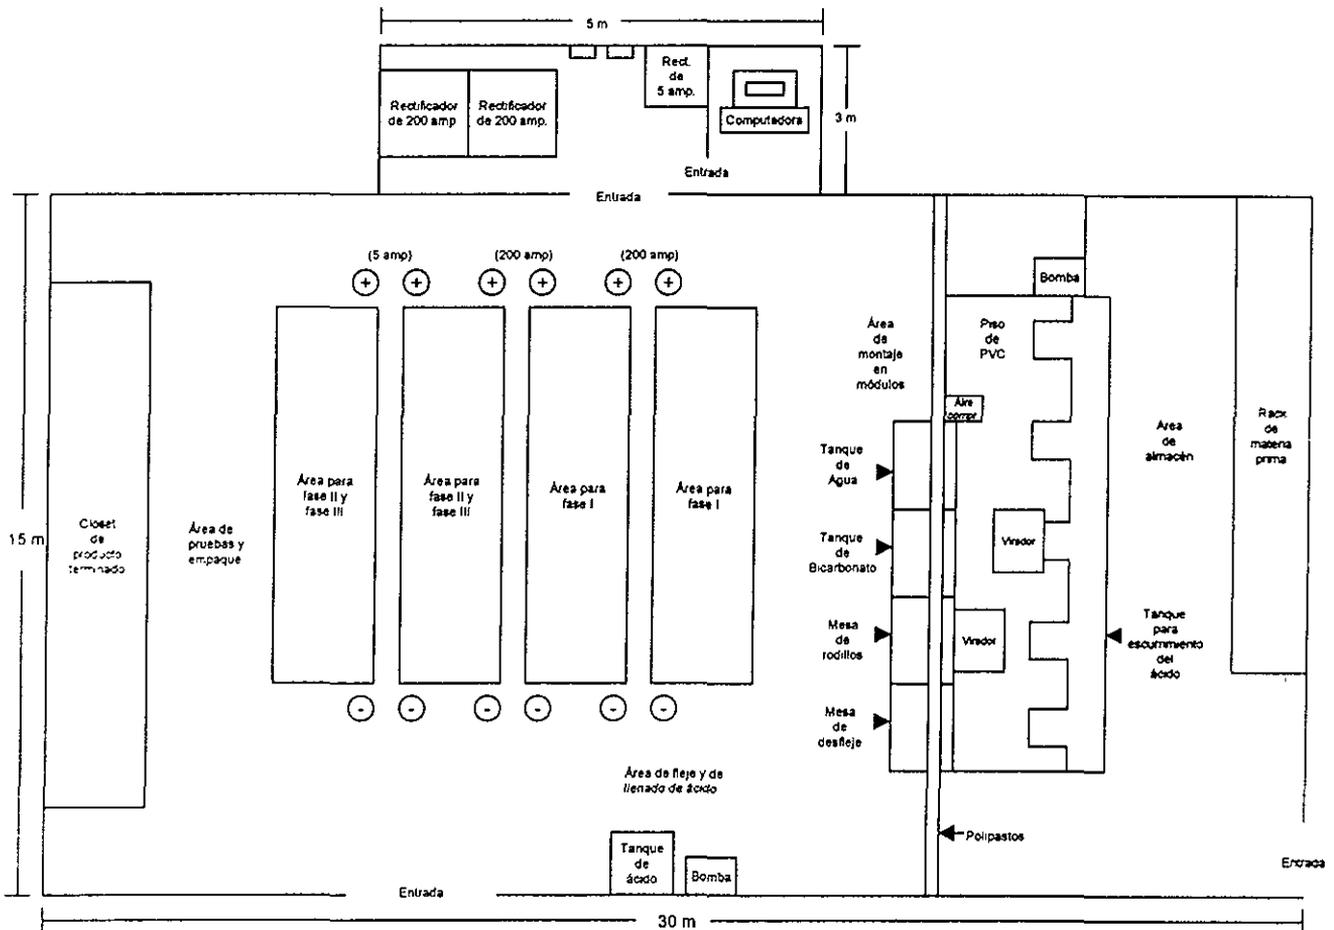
Plano de Distribución de Planta del proceso actual en Brasil
